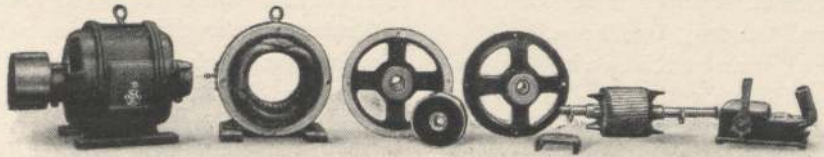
Drehstrom-Kurzschlußankermotor mit Stern-dreiecksschalter und seine Einzelteile.
